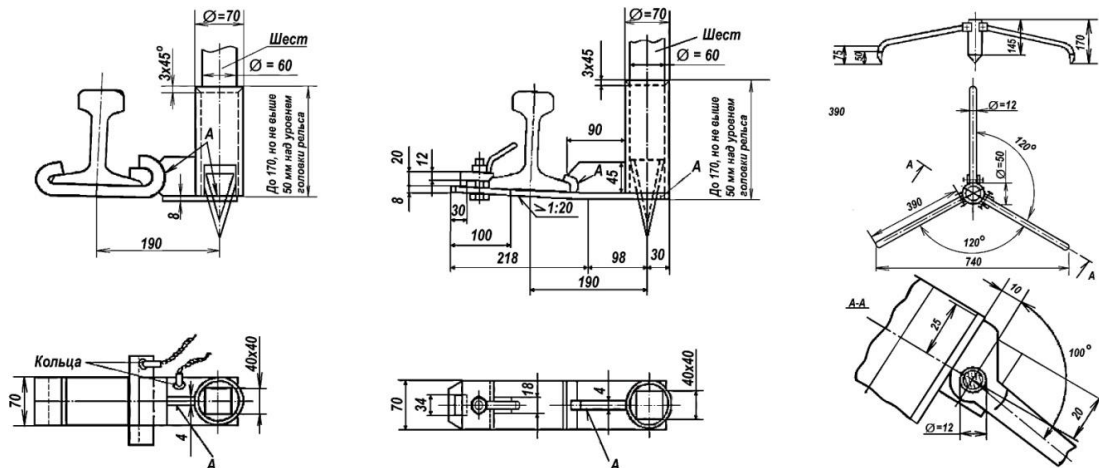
Приспособления для закрепления шеста переносного сигнала
